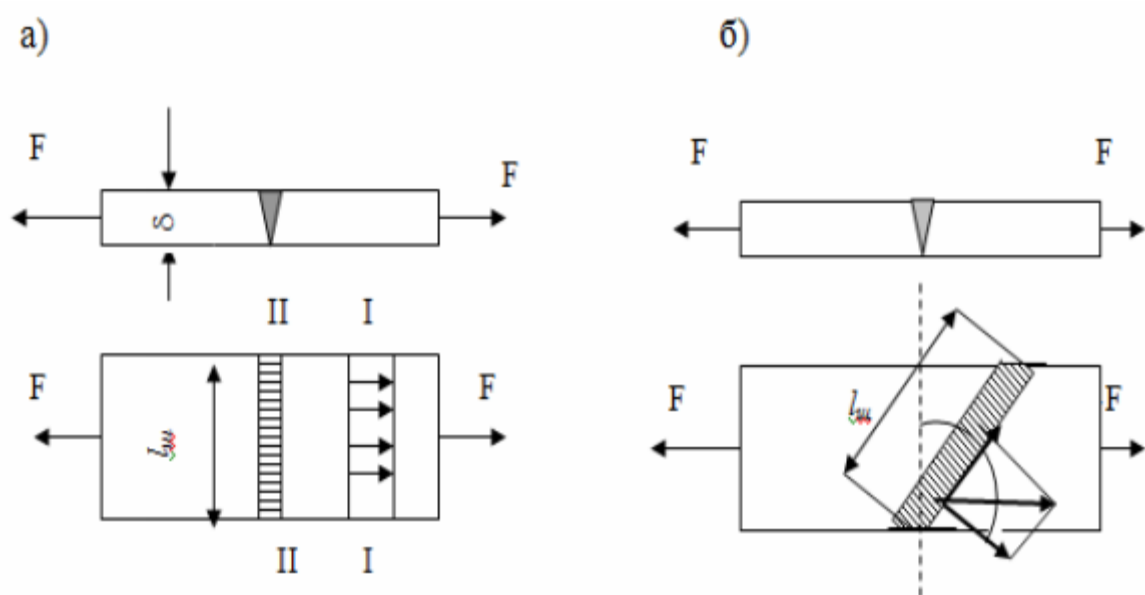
Сварные соединения встык, выполненные швами:
